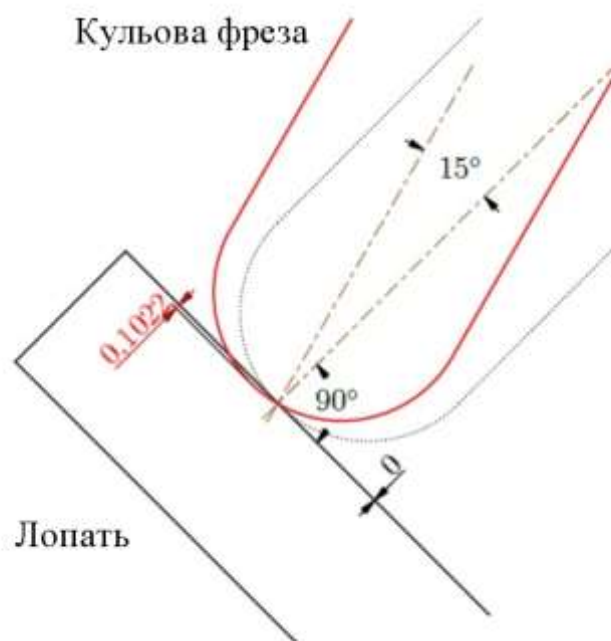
Умови залучення для 15° кута нахилу між поверхнею робочої деталі та 12 мм кульовою фрезою.
